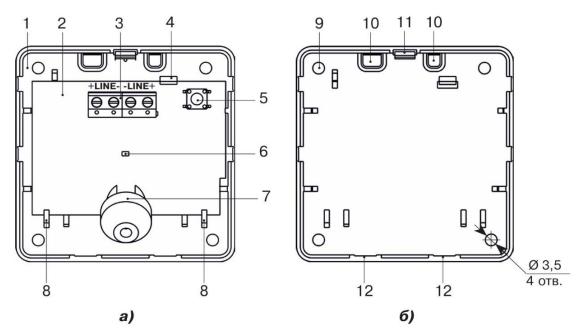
Основание корпуса с печатной платой: а – вид сверху (без крышки), б – основание
